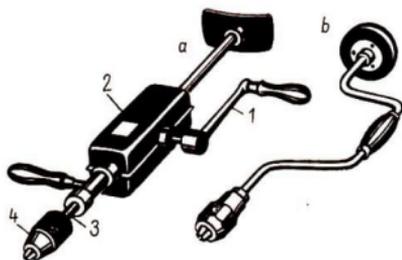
Handbohrmaschine (a) und Bohrwinde (b)
